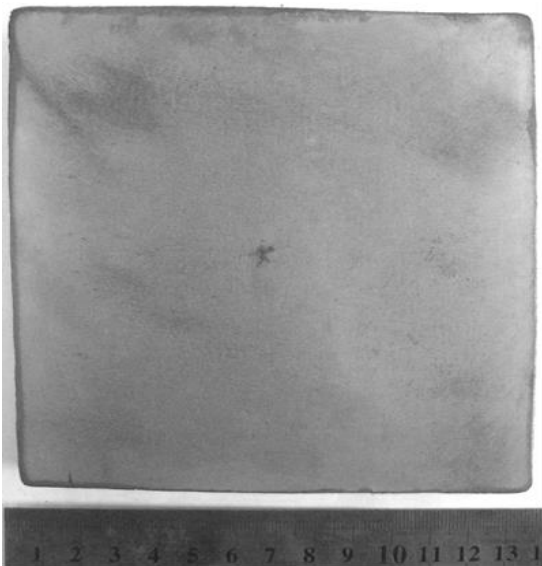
Макроструктура непрерывнолитой заготовки сечением 130x130 мм из стали 45
